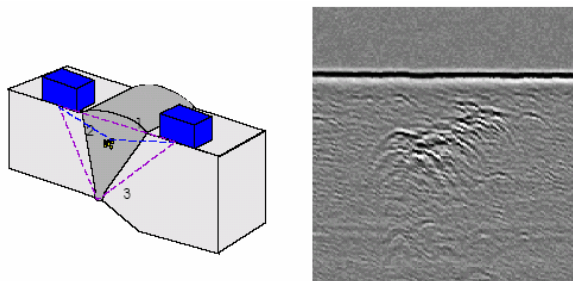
Zobrazení vady neprozetitelného kování při zkoušení tupého svaru technikou TOFD.
